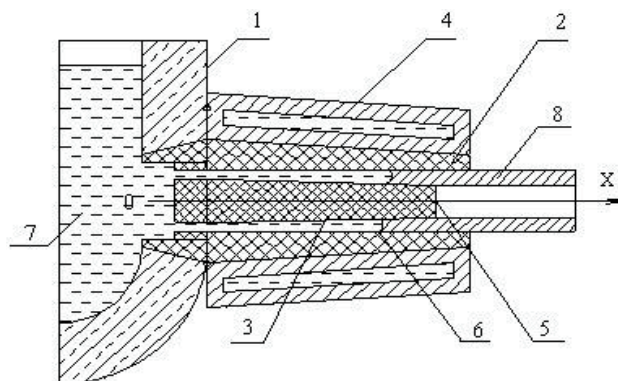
Конструкция узла кристаллизации машины непрерывного литья полых заготовок из медных сплавов: 1 - корпус металлоприемника; 2 - графитовая втулка кристаллизатора; 3 - дорн для формирования внутренней поверхности заготовки; 4 - водоохлаждаемый кожух кристаллизатора; 5 - торец дорна; 6 - положение фронта затвердевания; 7 - расплав; 8 - полая заготовка
